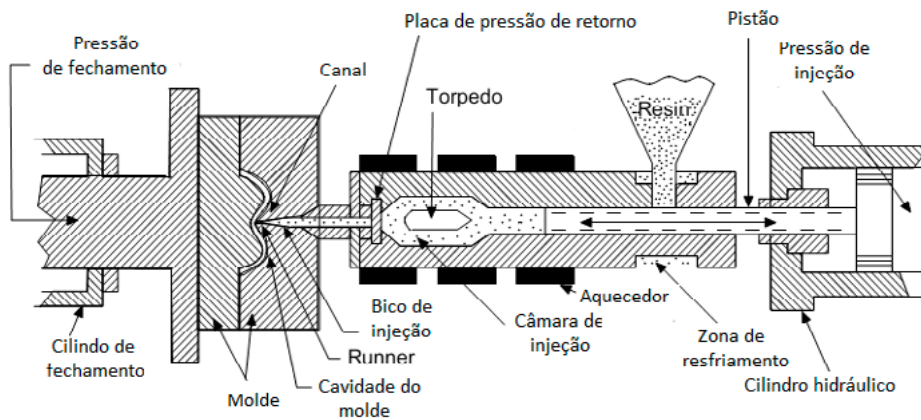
Desenho esquemático de um equipamento de moldagem por injeção.
